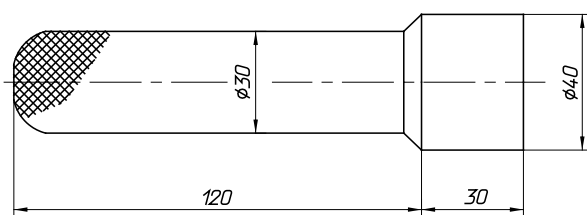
Оправка для выпрессовки теплопередающего элемента
